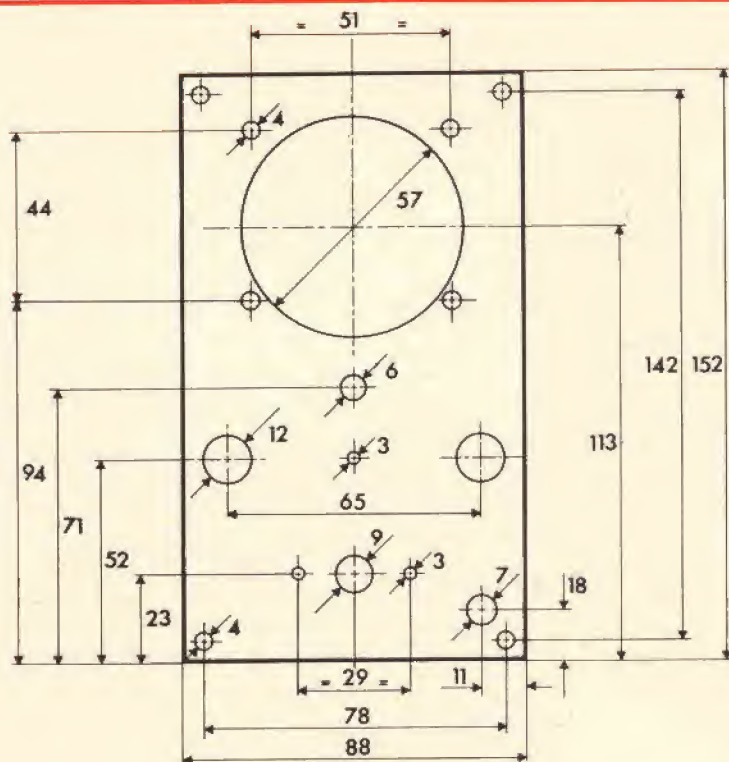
Piano di foratura del pannello frontale scala 1/2.
